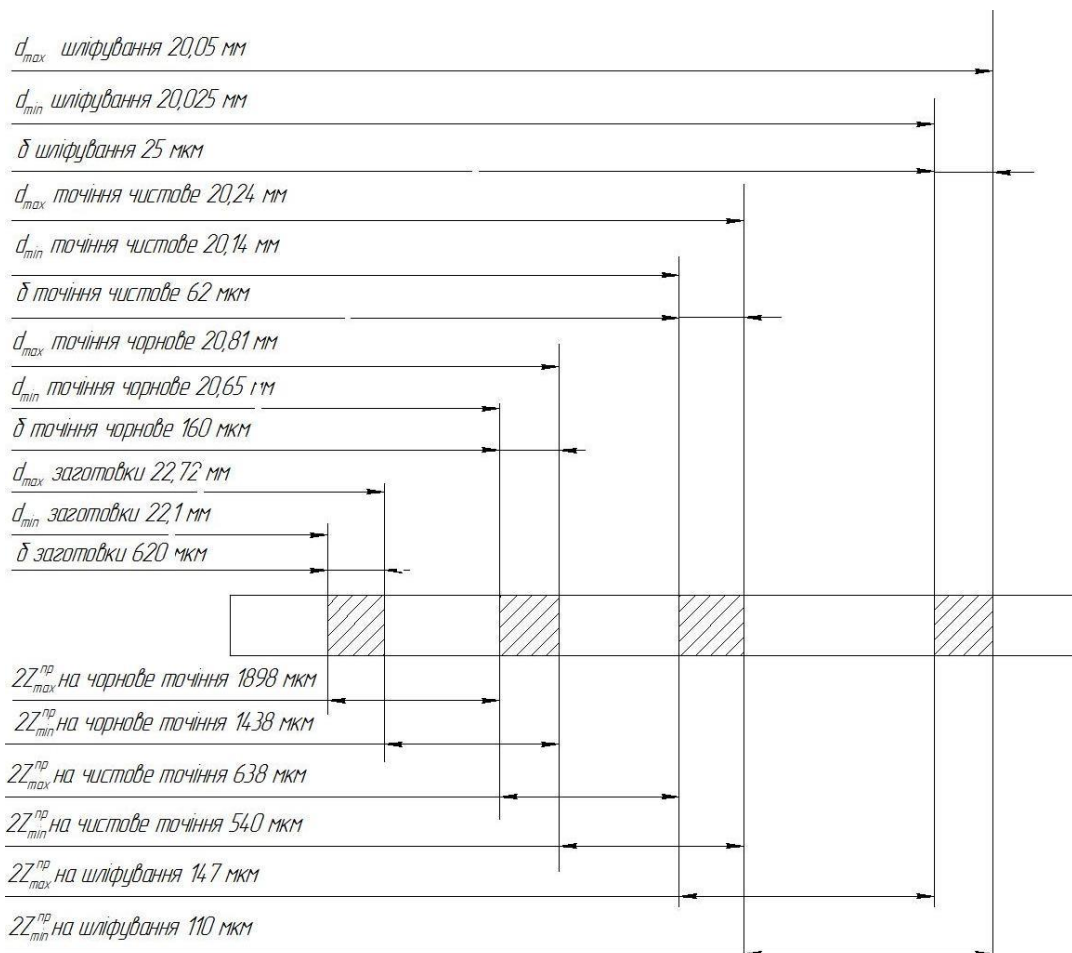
Схема графічного розміщення припусків і допусків на обробку валу $\varnothing 20h9$ деталі «Вал шестерня»
